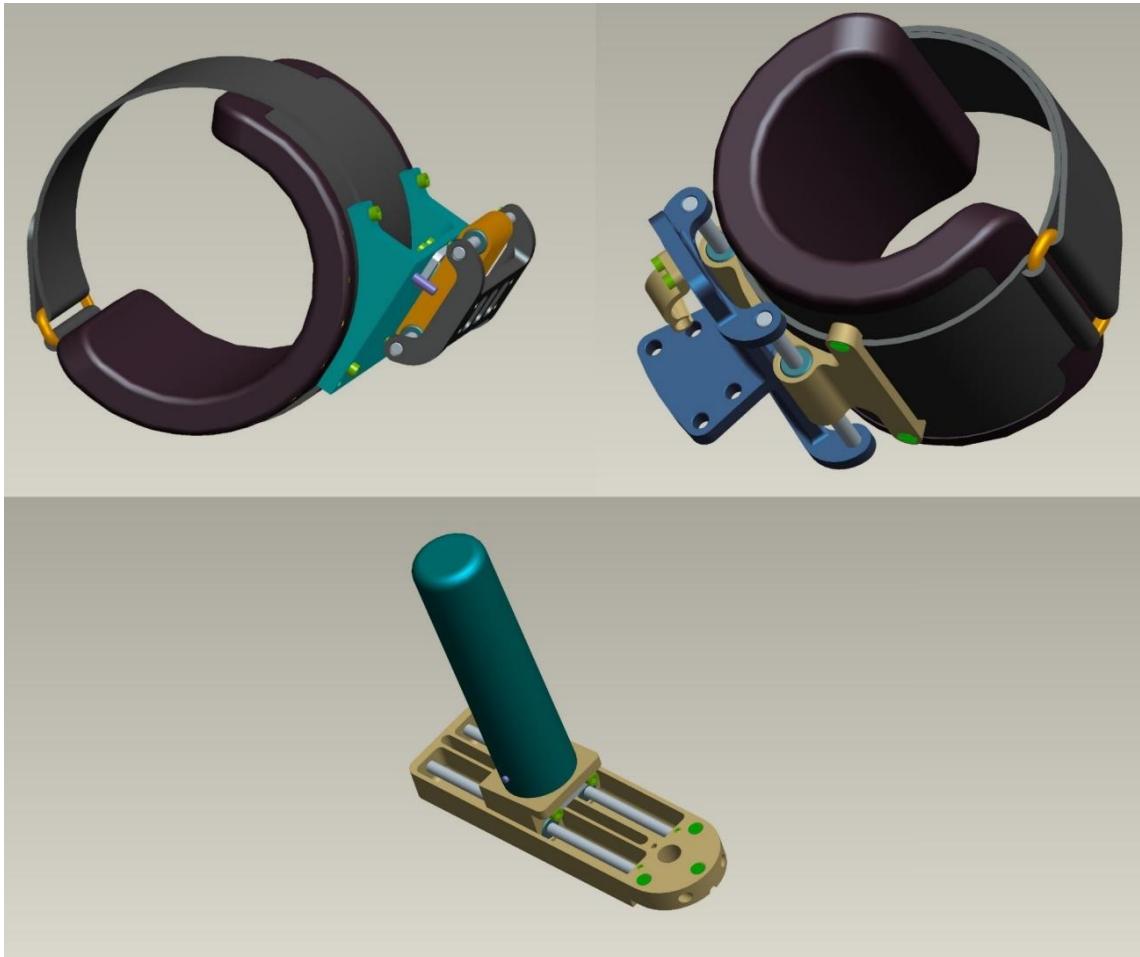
Viste assonometriche dei collegamenti al braccio, all'avambraccio e alla mano dell'utente.
